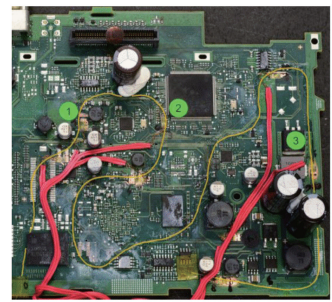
OFDR 用于 PCB 应变监测<sup>[41]</sup>
